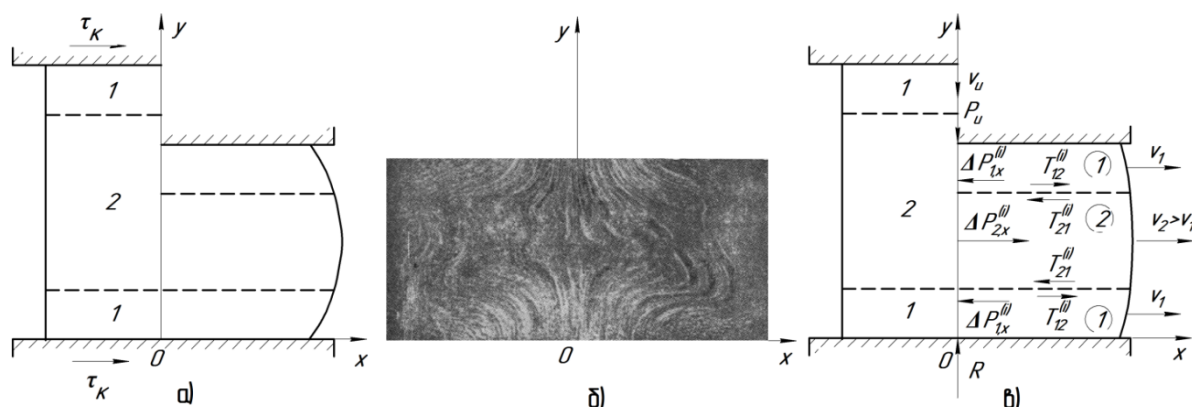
Схема процесса бочкообразования боковой поверхности заготовки:
